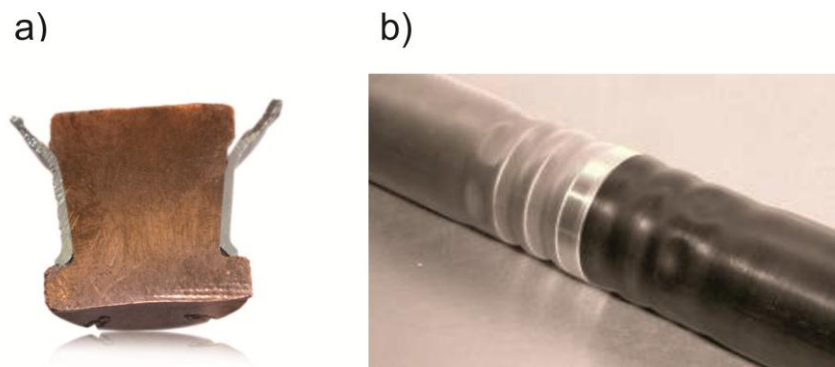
Połączenie elementów rurowej konstrukcji z lekkich stopów aluminium: a) rama, b) łącznik [12]
